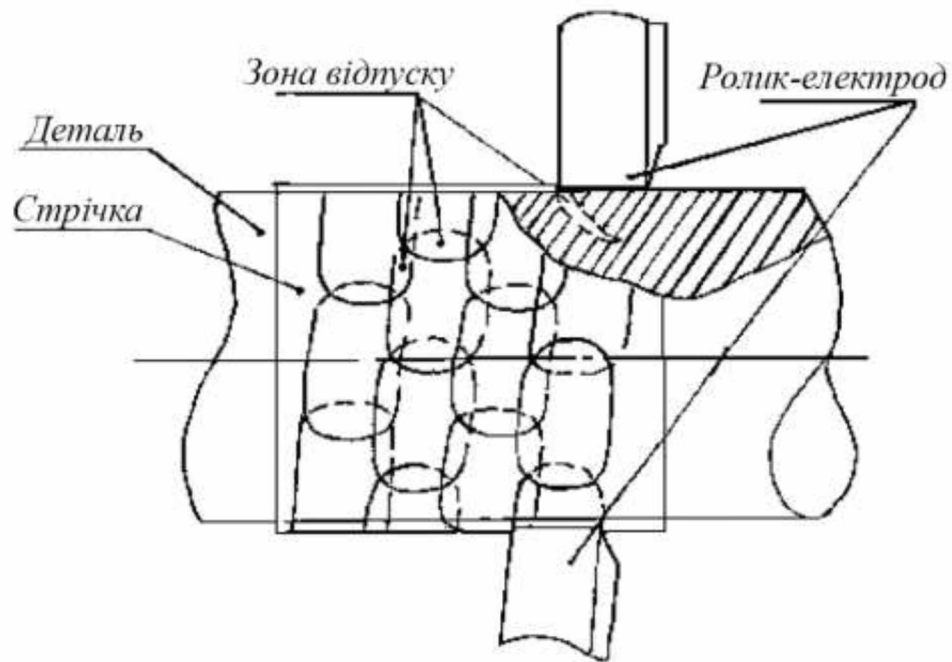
Місця розташування зварювальних точок при контактному зварюванні
